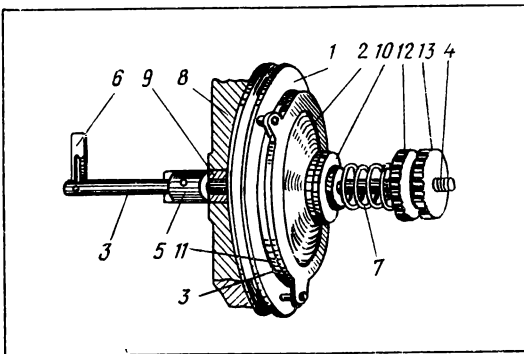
Наматыватель кинопроектора КПТ-1: 1 — шкив; 2 — муфта; 3, 10 — фланцы; 4 — вал; 5 — шпонка; 6 — защелка; 7 — пружина; 8 — кронштейн-крестовина; 9 — втулка; 11 — фрикционная шайба; 12 — гайка; 13 — контргайка
